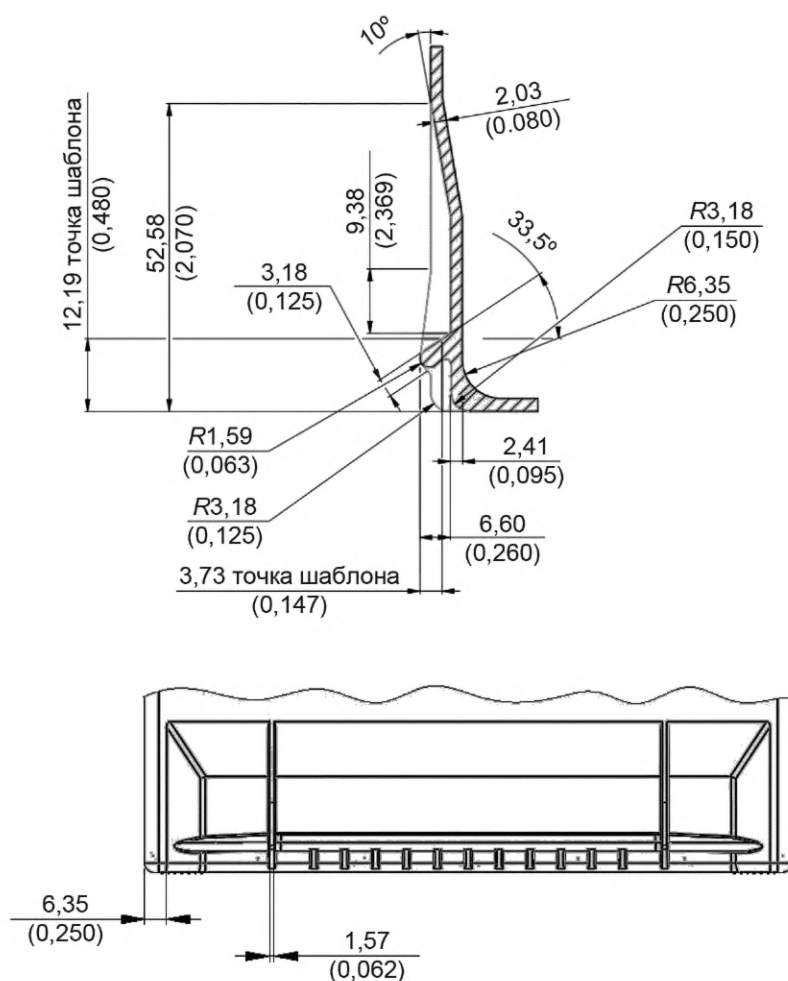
Форма и размеры углублений на корпусе, образующих бортик на короткой стороне корпуса батареи
